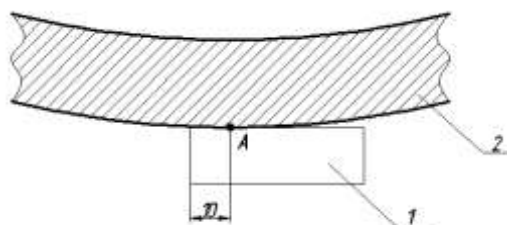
Схема встановлення повзуна на початку зварювання
